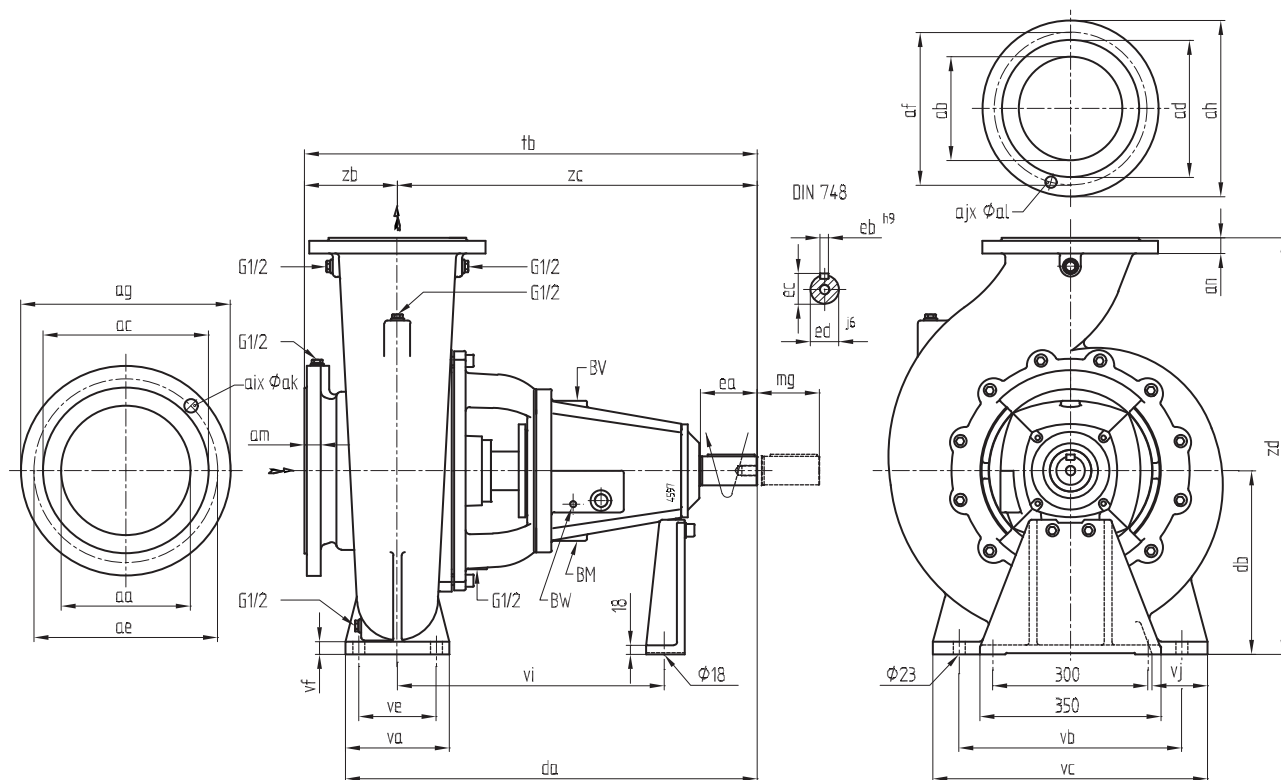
Dimensões da bomba - grupo de rolamento 4.
